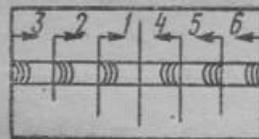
Сварка длинных швов обратнo-ступенчатым способом от середины к концам шва
